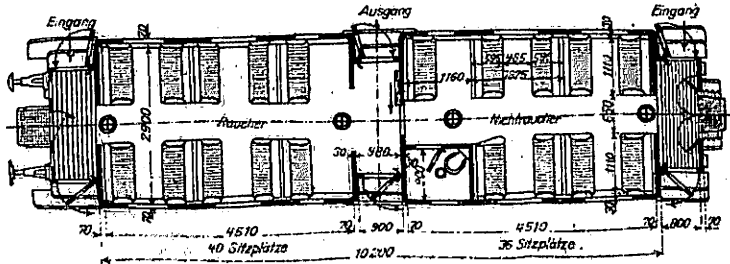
Grundriß eines Württ. Di-Wagens der bisherigen Bauart.
